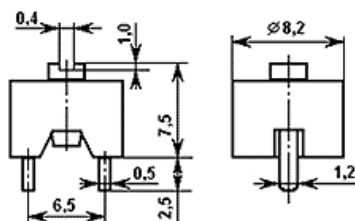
Габаритні розміри конденсатора TZ03Z100F169
